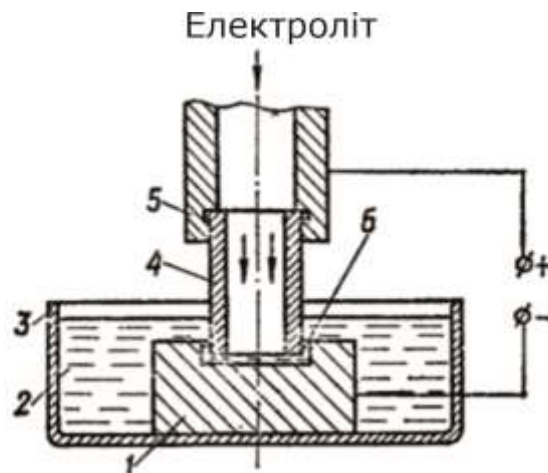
Схема електроерозійно-хімічної обробки.
